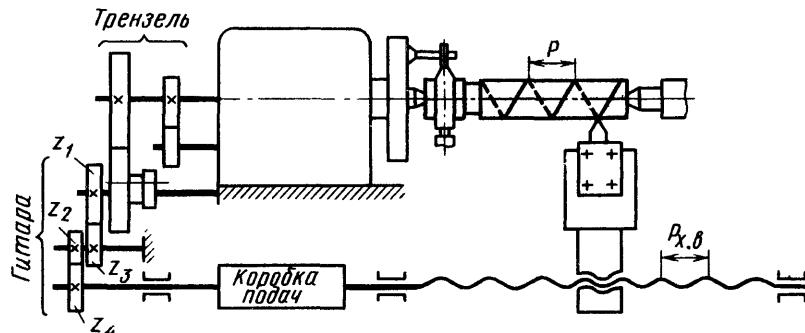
Упрощенная кинематическая схема токарного станка
